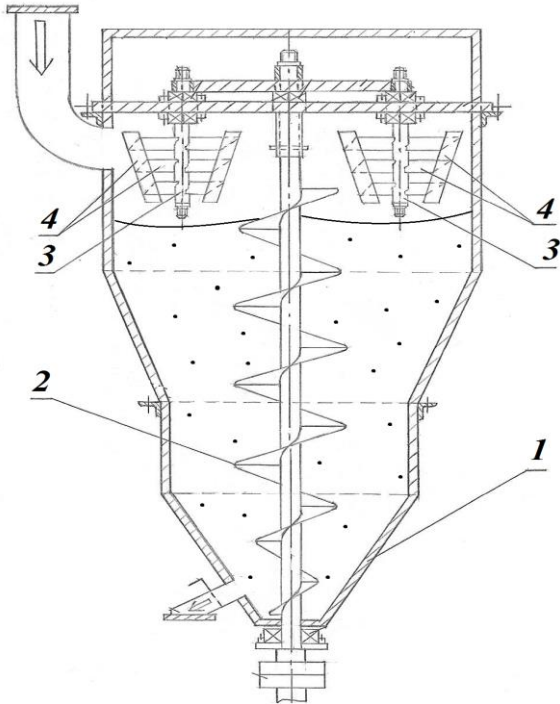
Конструктивна схема змішувача інгредієнтів комбікормів: 1 – корпус; 2 – шнек; 3 – консольні вали; 4 – двохплощинні лопатки.
